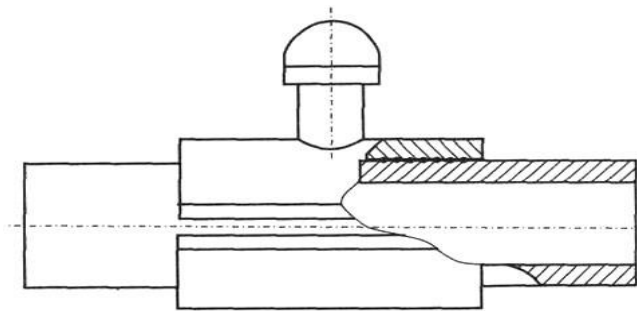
Качественно выполненное сварное соединение с ЗН
